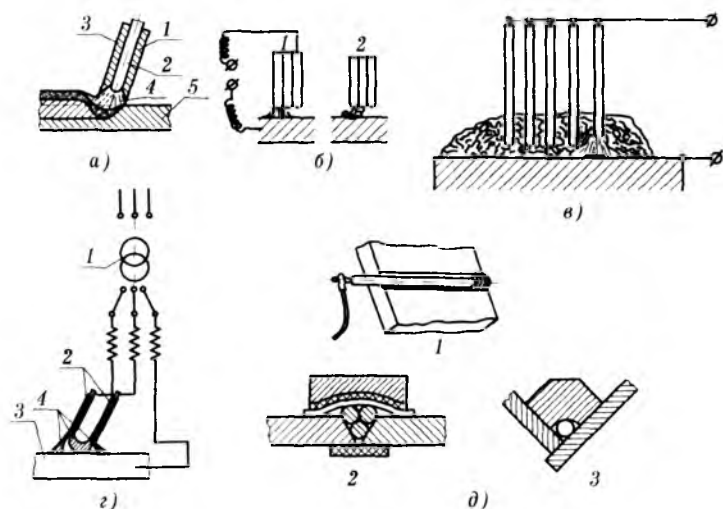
Усовершенствованные методы ручной сварки:
